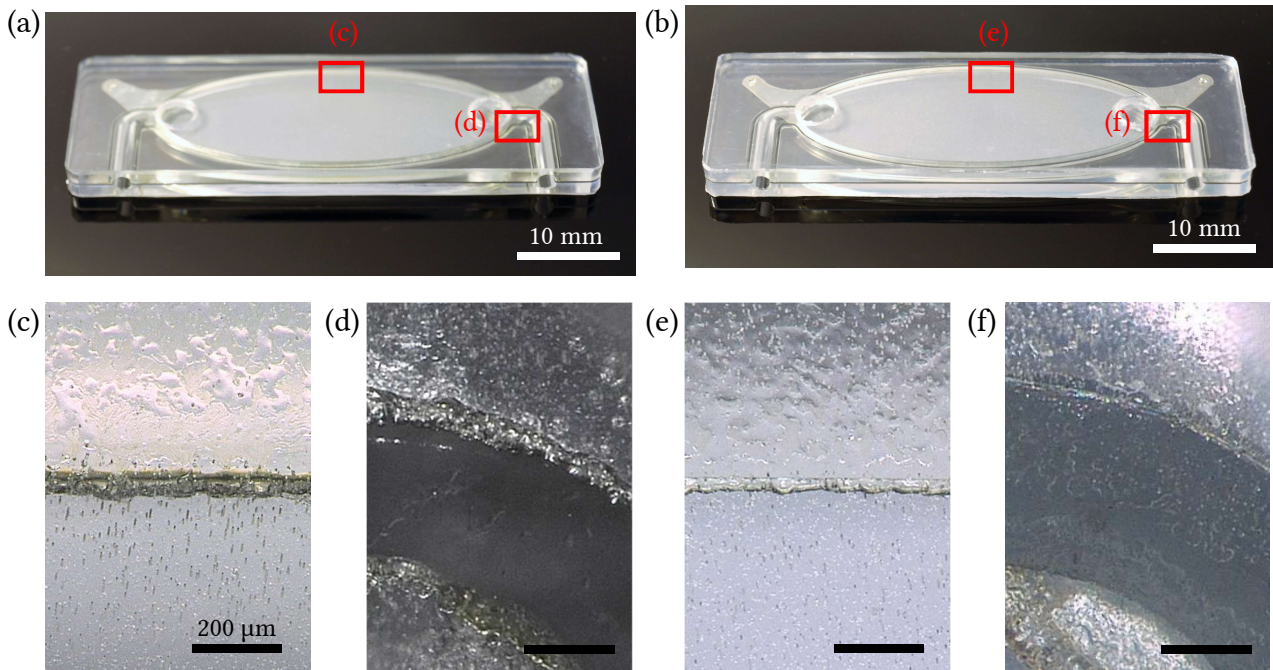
Durch Laserdurchstrahlschweißen gefügte 800 µl-MBR. (a) MBR aus PC, (b) MBR aus PET, (c) der obere Bildbereich stellt die transparente Schweißnaht der MBR aus PC dar, in welcher keine Membranporen mehr zu sehen sind, (d) die Schweißnaht des MBR aus PC ist an der 90°-Biegung ebenfalls transparent, (e-f) die Schweißnähte des MBR aus PET sind auch transparent. Bei diesen Bildern entspricht der Maßstabsbalken einheitlich 200 µm.
